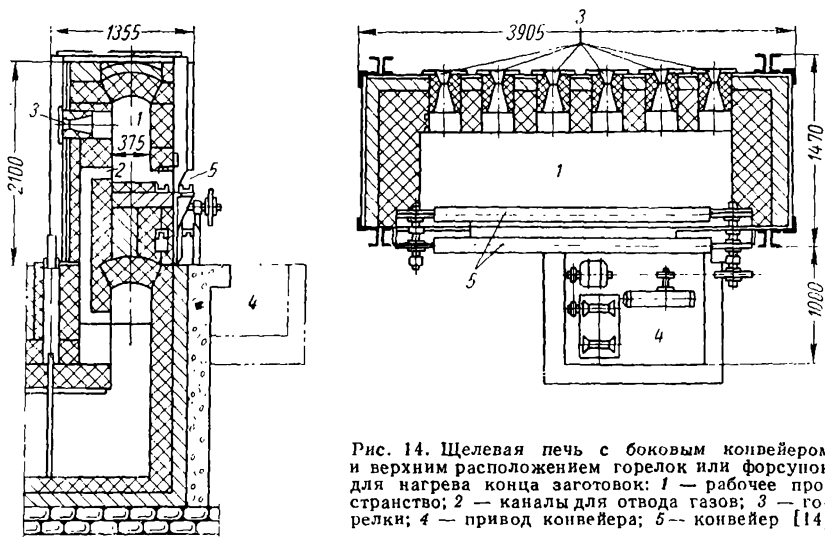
Щелевая печь с боковым конвейером и верхним расположением горелок или форсунок для нагрева конца заготовок: 1 — рабочее пространство; 2 — каналы для отвода газов; 3 — горелки; 4 — привод конвейера; 5 — конвейер [14]
